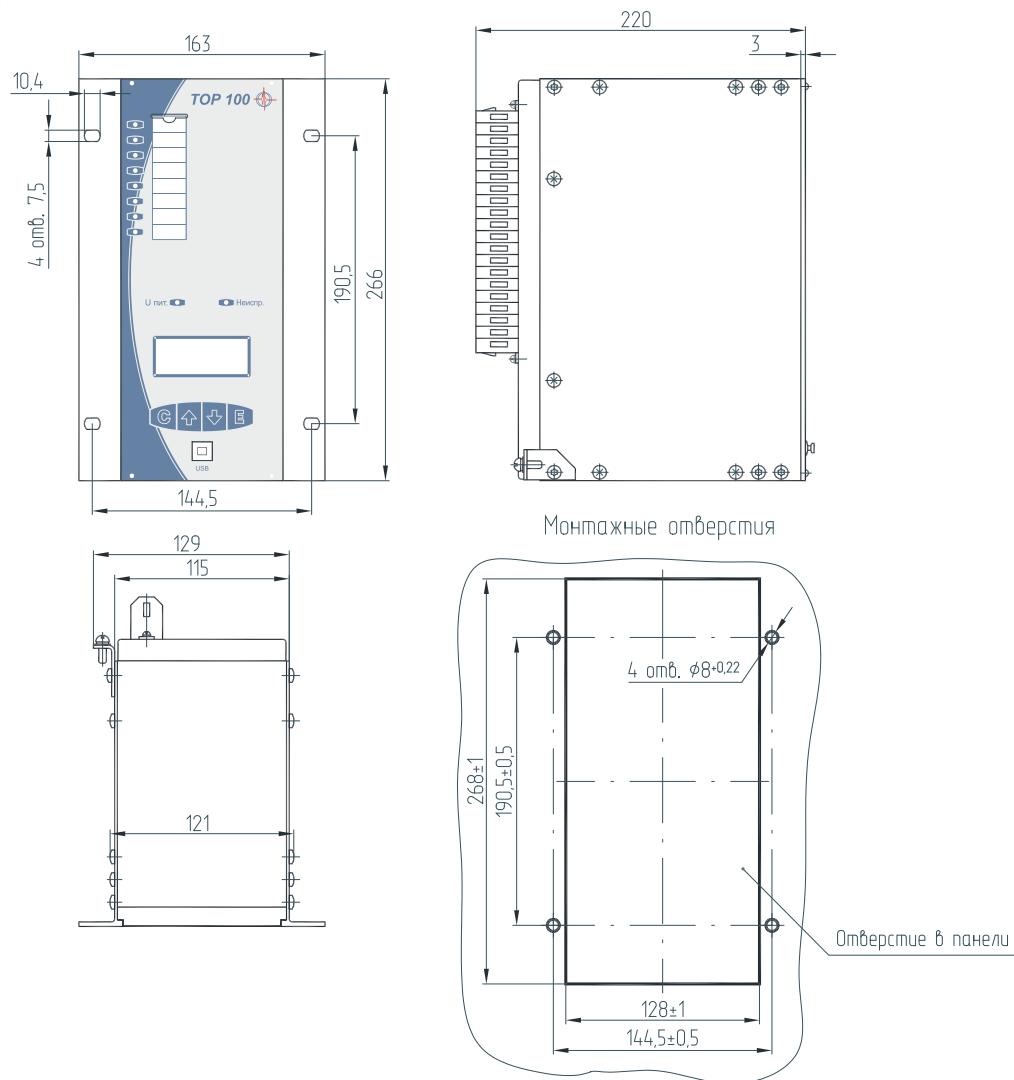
Габаритные и установочные размеры для утопленного монтажа
